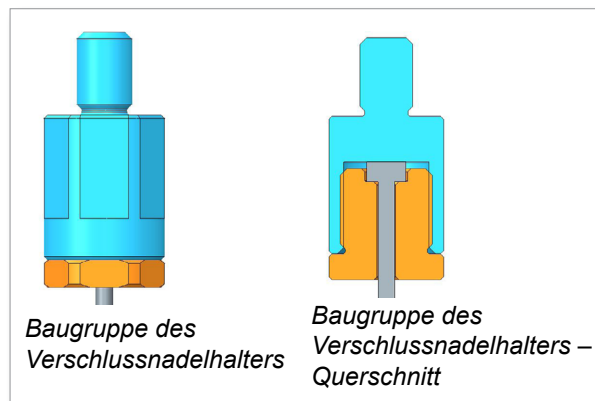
Baugruppe des Verschlussnadelhalters
